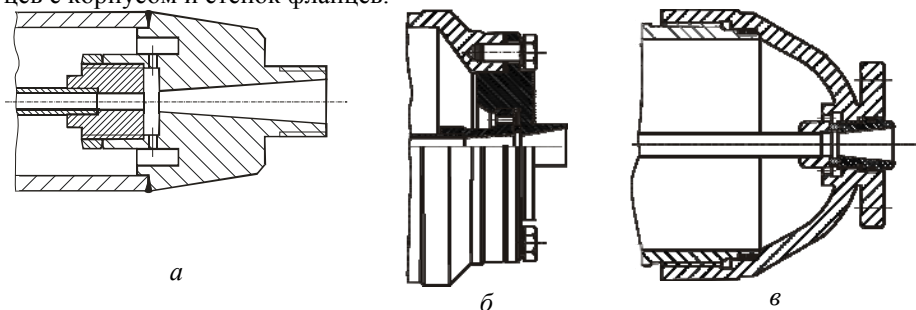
Варианты конструктивных соединений фланцев с корпусом гасителя колебаний жидкости: а - сварное; б - болтовое; в – резьбовое
